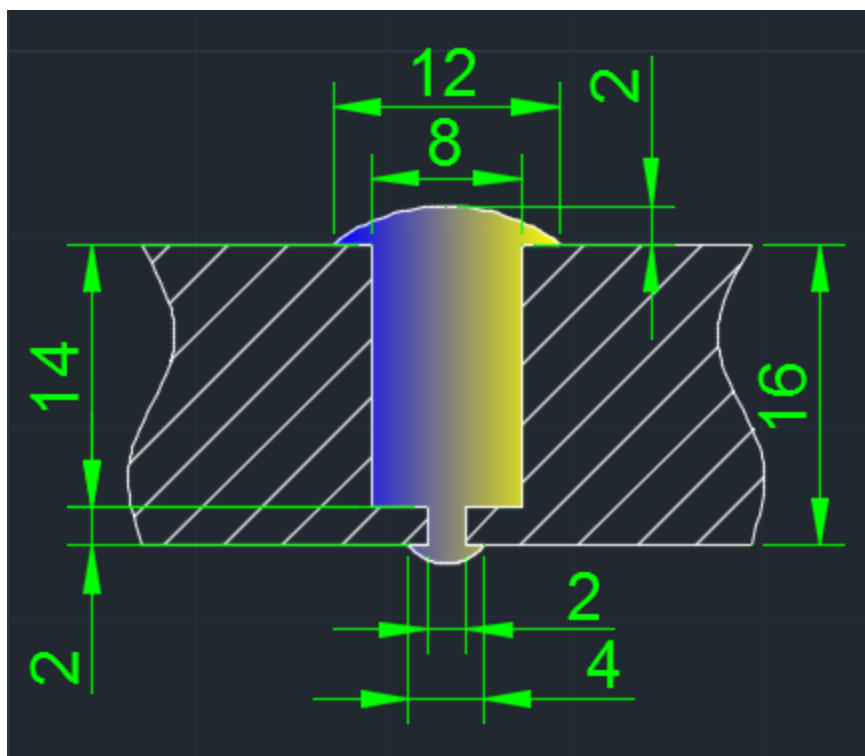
Сечение сварного стыка модели с щелевой разделкой кромок
